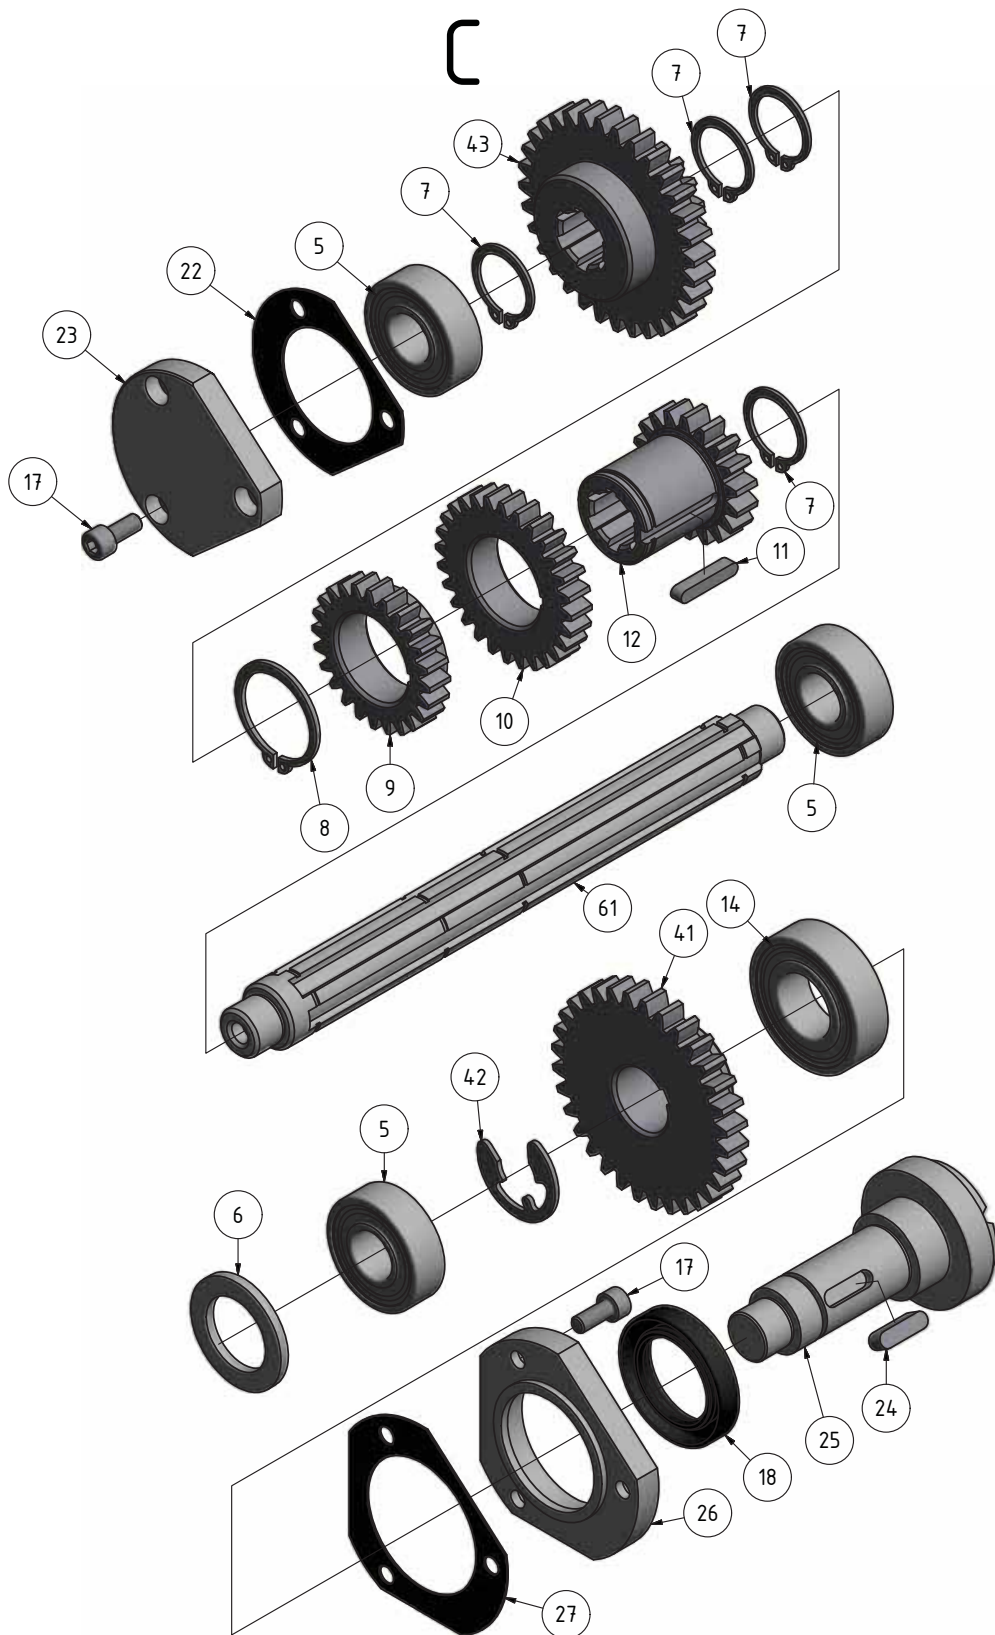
Vorschubgetriebe 5-6 - Feed gear 5-6
